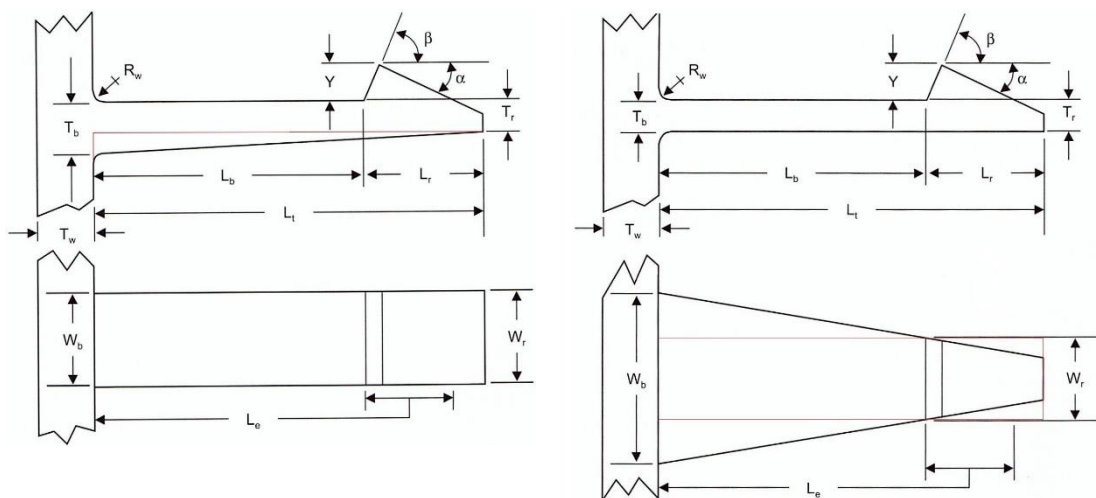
Cantilever Beam Tapered in Thickness* e *Cantilever Beam Tapered in Width*.
